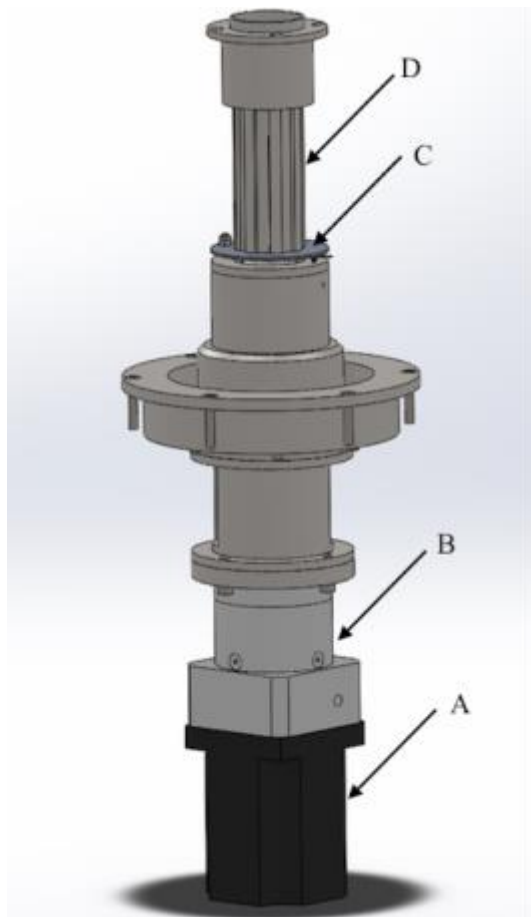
Modelo SW do sistema de Transmissão de rotação em Translação Linear. A-Motor passo-a-passo; B-Redutor 8:1; C- Placa portadora de um MicroSwitch; D- Castanha mecânica
